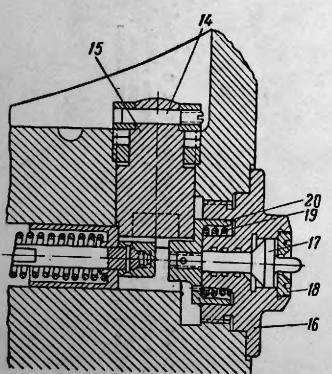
Жесткое положение бойка: 14—винт (1-82); 15— переключатель (1-81); 16— корпус бойка (1-27); 17— боек (1-28); 18— упор (1-28); 19— пружина бойка (1-29); 20— основание бойка (1-88)
